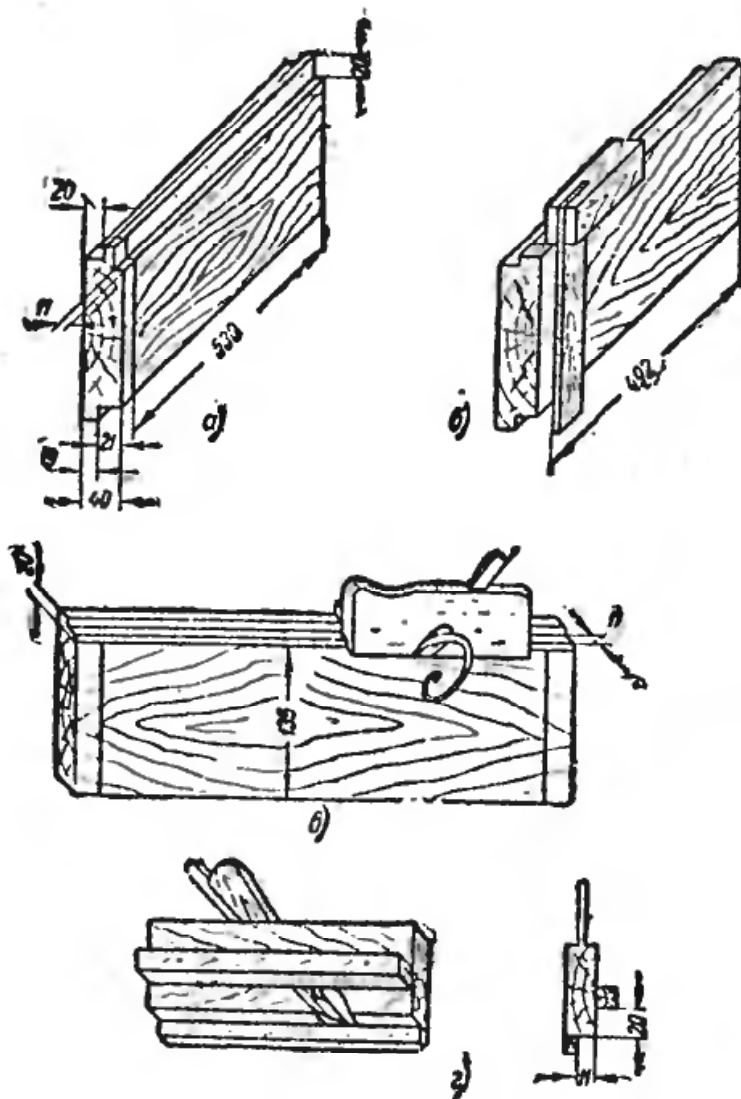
Разметка и отборка рамочных фальцев: *a* и *б* — разметка; *в* — отборка фальцев зензубелем; *г* — зензубель с установкой бокового порожка (*л*).
